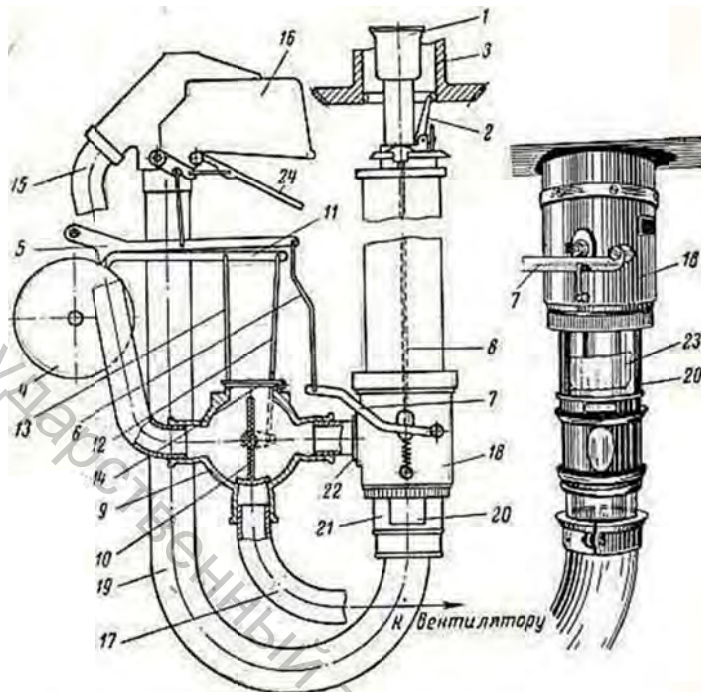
Механизм пневматической оттяжки с автоматической вывороткой изделия
